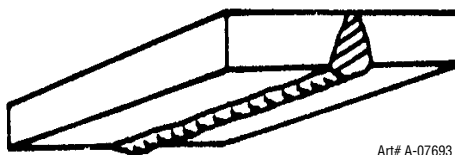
Position horizontale, soudure par aboutement
